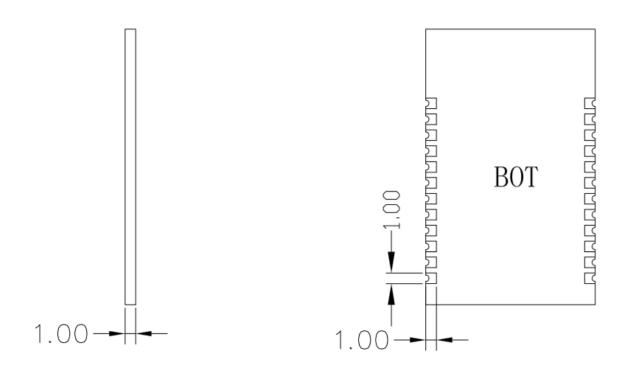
注:图 11 所示厚度仅表示 PCB 板厚度,模块整体厚度 2.5mm。
